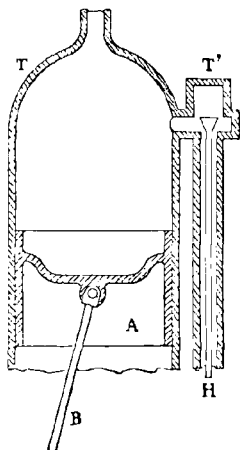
Moteur à éther de pétrole pour la bicyclette Millet.
